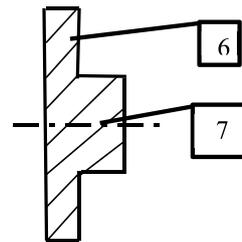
Схема датчика: 6 – пластина; 7 – выступ пластины
